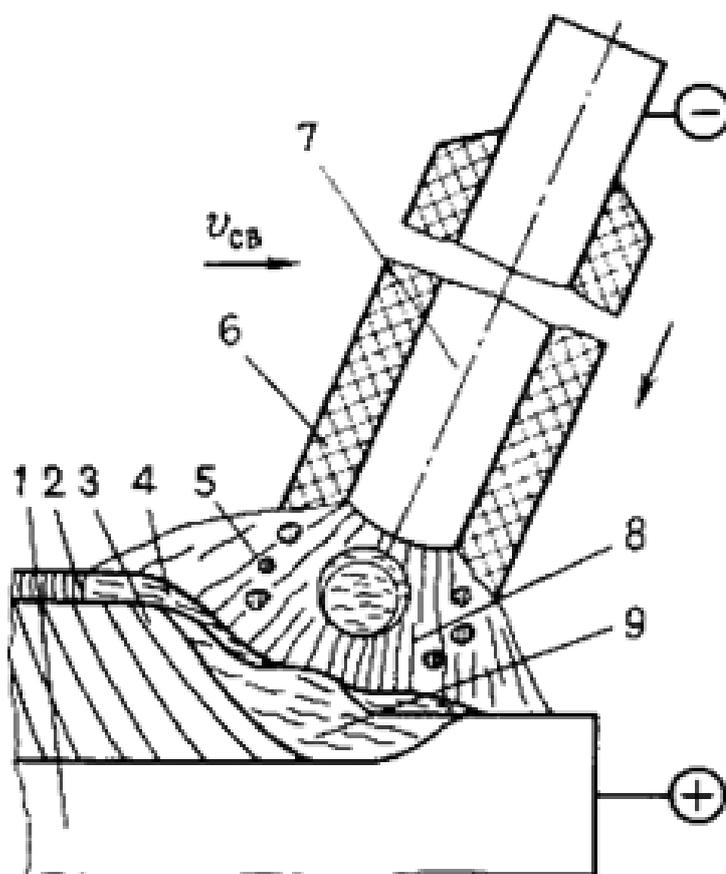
Схема процесса сварки металлическим покрытым электродом
